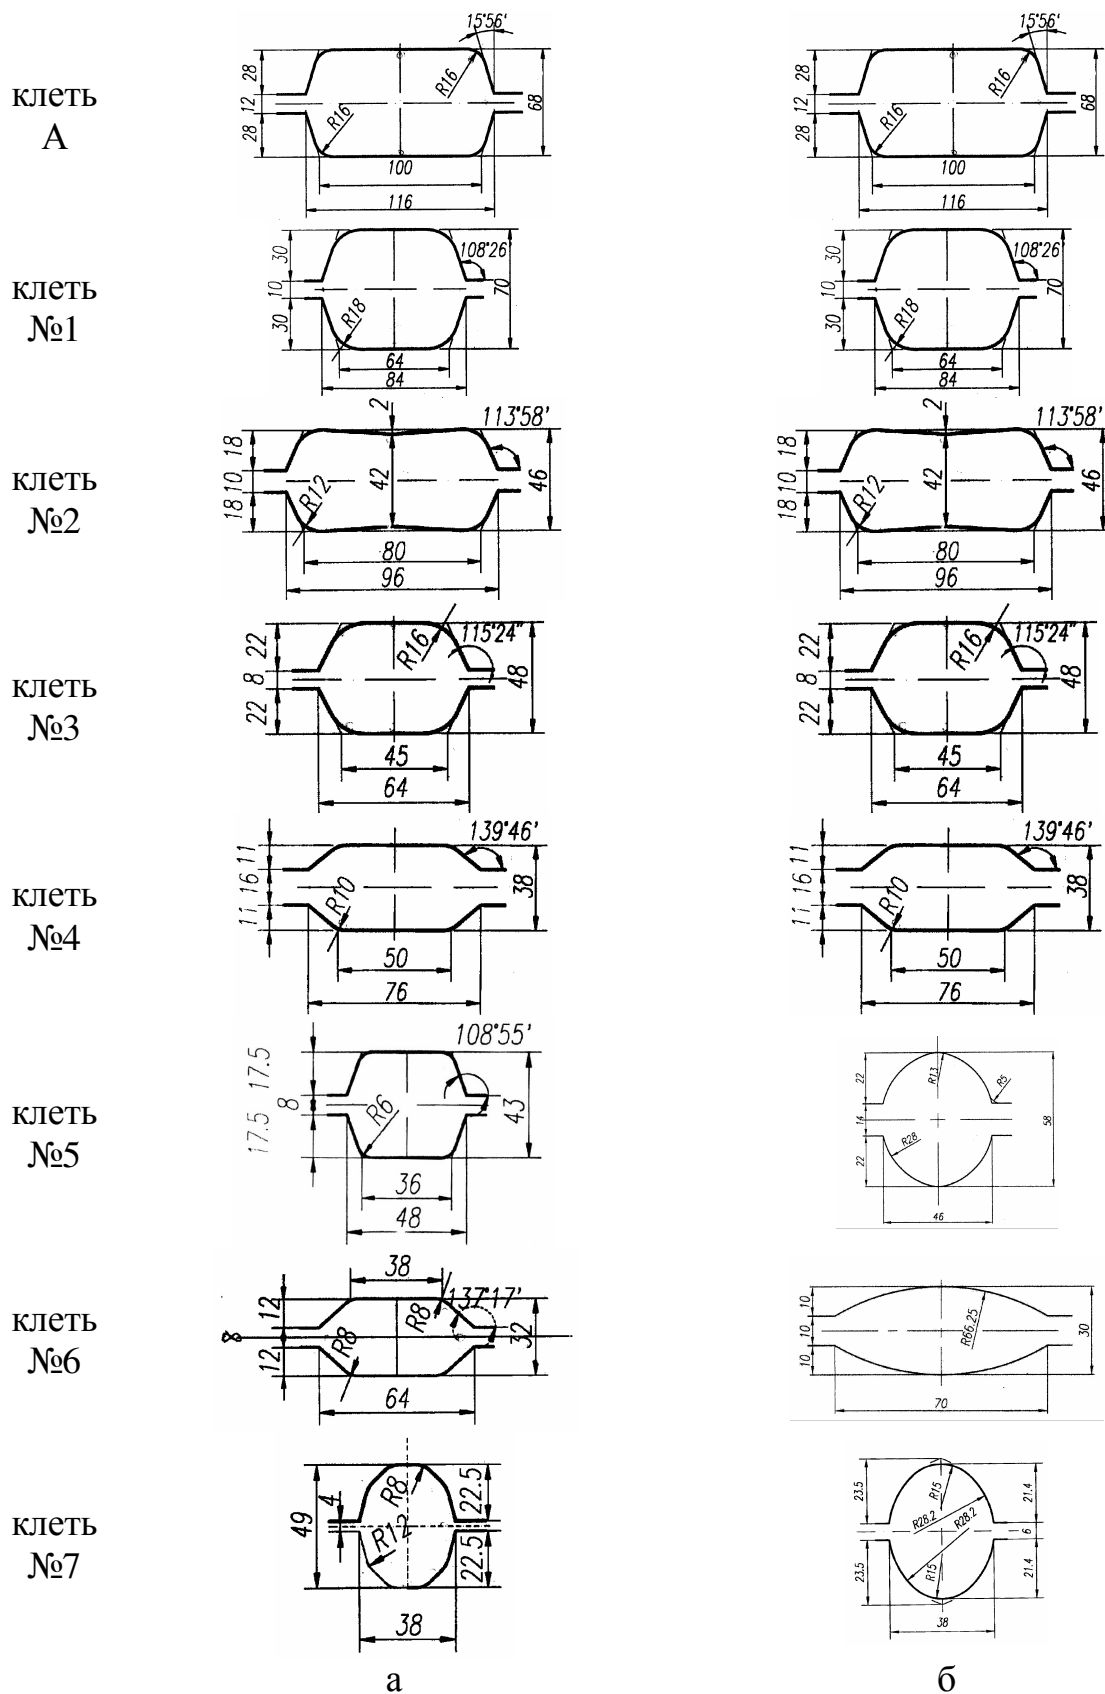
Калибровка валков черновой группы клетей мелкосортного стана 250-2
